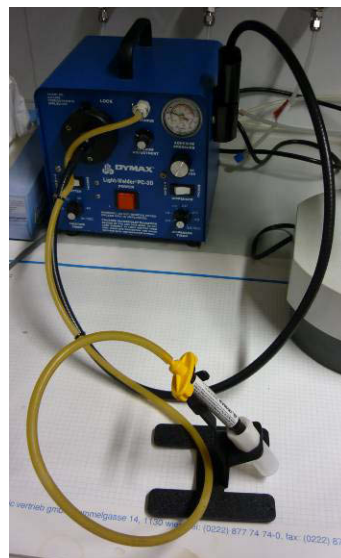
Abbildung des Light Welder PC-3D mit angeschlossener Kleberspritze.
